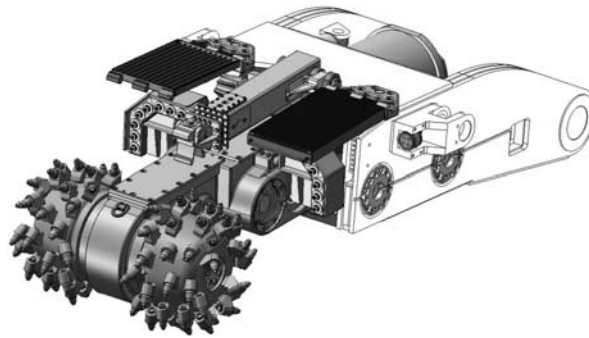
Исполнительный орган с двумя поперечно-осевыми режущими барабанами
